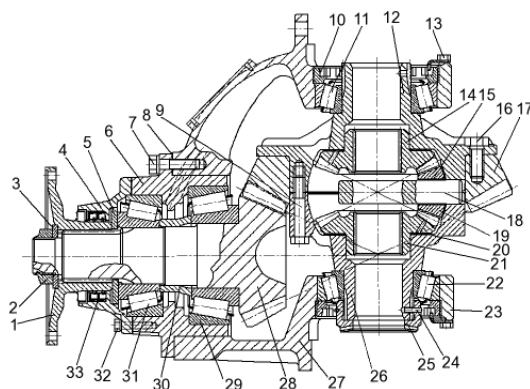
Главная передача заднего моста: 1 – фланец ведущего вала; 2 – гайка; 3, 5, 20 – шайбы опорные; 4 – крышка подшипников; 6 – стакан подшипников; 7, 9, 16, 32 – болты; 8 – регулировочные прокладки; 10 – регулировочная гайка; 11, 22, 29, 31 – подшипники; 12, 26 – чашки дифференциала; 13 – винты; 14, 21 – полуосевые зубчатые колеса; 15 – бронзовая втулка; 17 – ведомое зубчатое колесо; 18 – крестовина; 19 – сателлит; 23 – крышка картера; 24 – кольцо стопорное; 25 – зубчатая муфта; 27 – картер главной передачи; 28 – ведущее зубчатое колесо; 30 – втулка регулировочная; 33 – манжеты
